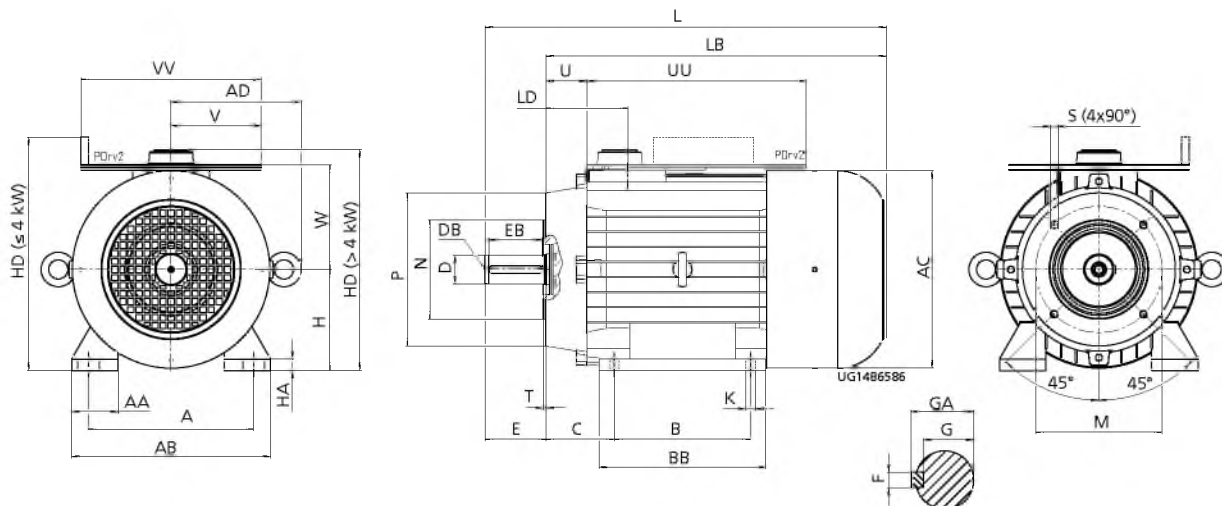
Двигатель с адаптером для PumpDrive 2 и фланцем FT с резьбовыми отверстиями (V18,...)
